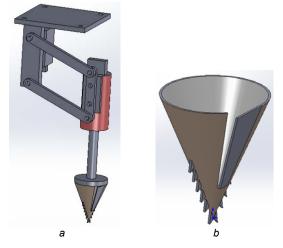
Конструкция грунтозаборника летающего робота: a - 3-D модель; b - нижняя (активная) часть Fig. 2. Design device taking away the soil on flying robot: a - 3D model; b - lower part of sampling system
